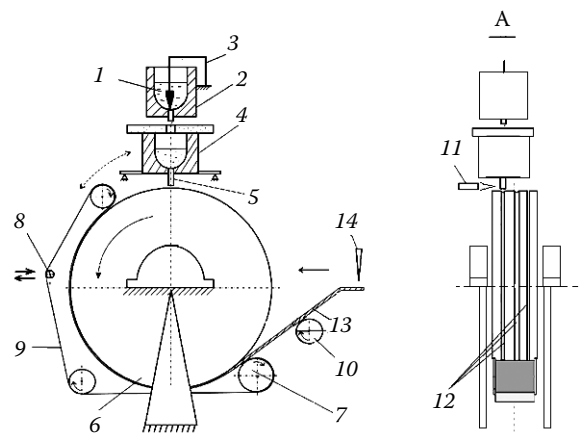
Схема непрерывного литья пруткового припоя из медно-фосфорных сплавов в кристаллизатор валок–лента: 1 – расплав; 2 – стопорный ковш; 3 – стопорно-поплавковое устройство; 4 – разливочный узел; 5 – литник; 6 – валковый кристаллизатор; 7 – опорный ролик; 8 – натяжной ролик; 9 – обкатная лента; 10 – выпрямляющий ролик; 11 – газовая горелка; 12 – каналы трапециевидного сечения; 13 – непрерывная заготовка; 14 – летучие ножницы для получения мерных прутков
